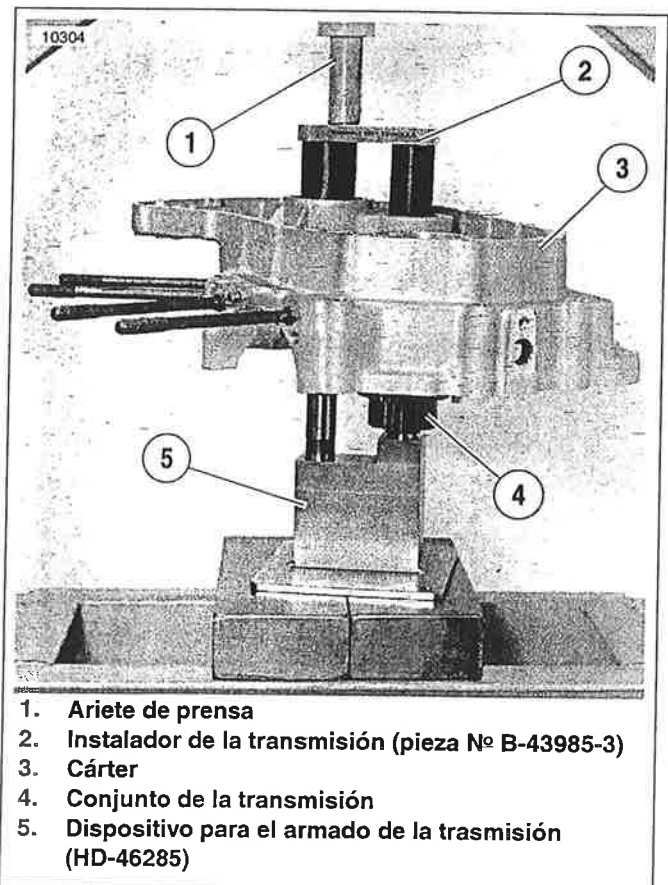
Presión de la transmisión en el cárter izquierdo
